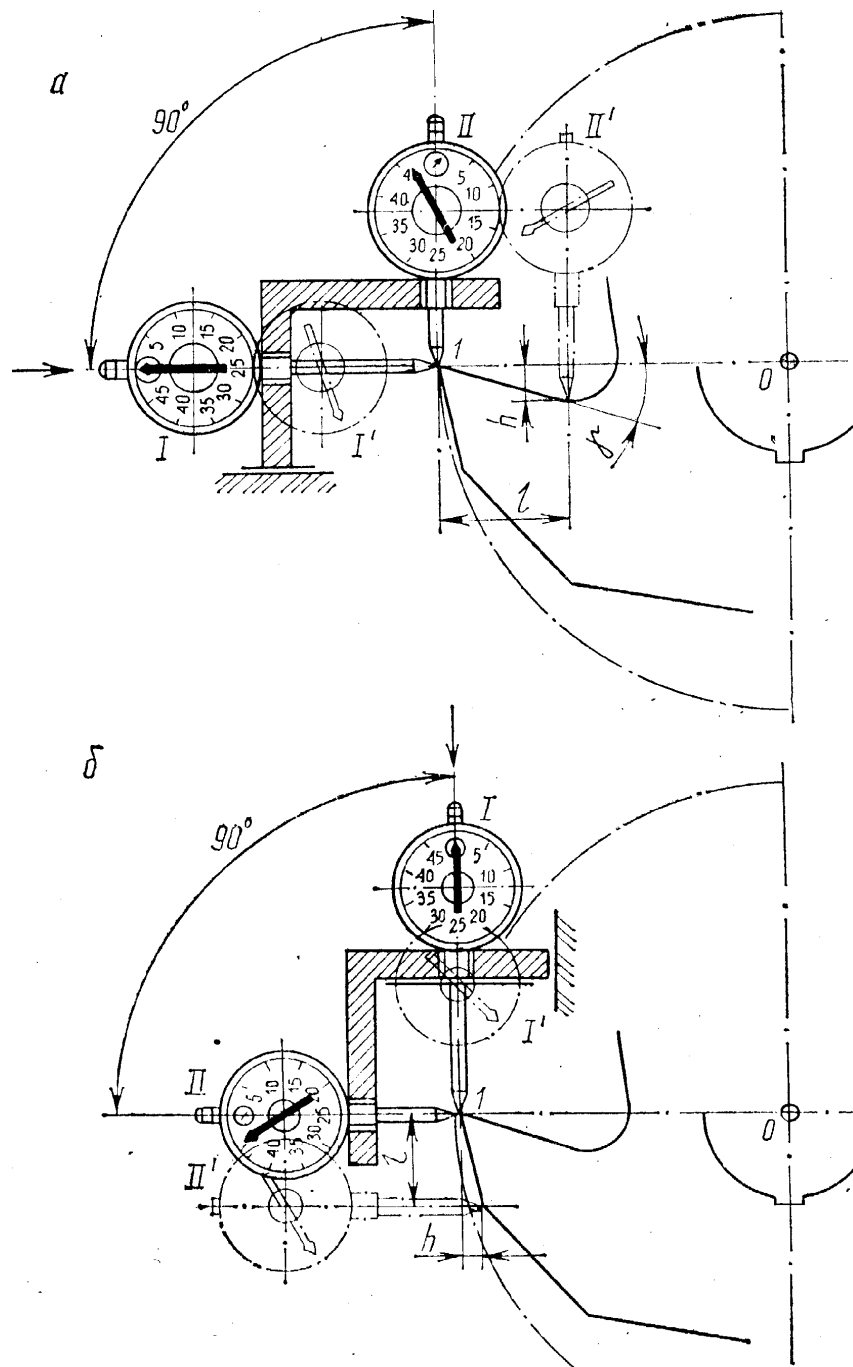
Схема вимірювання кутів фрези методом координат:
